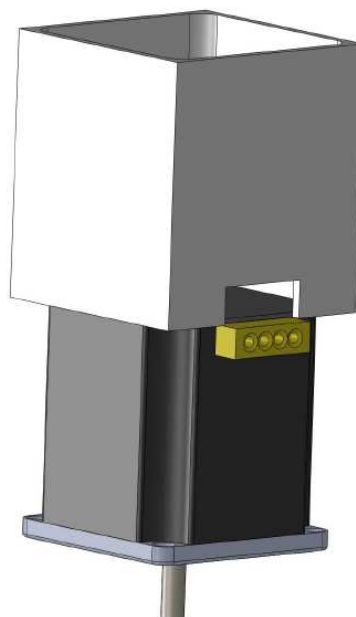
Montagem Motor de Passo e Cabine p/ Driver's
